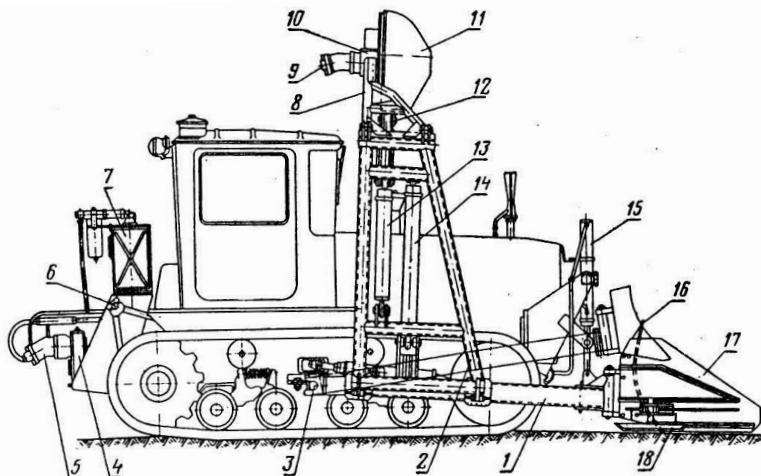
Каналоочиститель МР-14 с фрезерным рабочим органом
